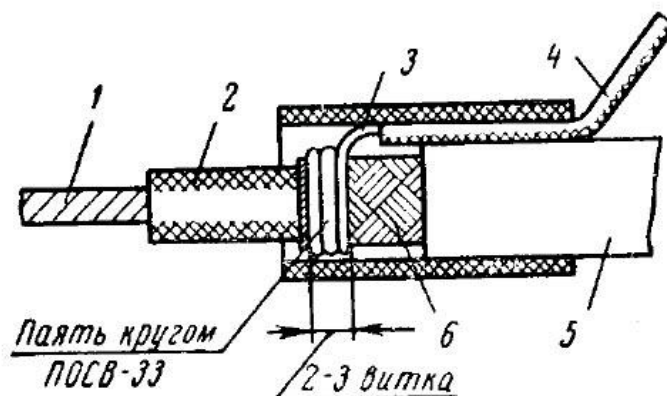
Намотка дополнительного провода на экранирующую оплетку:
